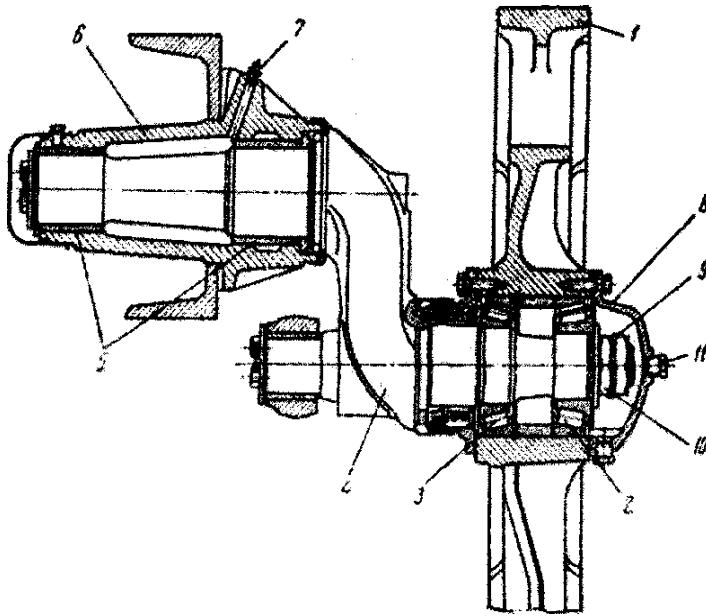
Напрявне колесо: 1 - напрявне колесо; 2, 3 - підшипники конічні; 4 - вісь колінчата; 5 - втулка; 6 - кронштейн напрямного колеса; 7 - оливниця; 8 - кришка; 9 - шайба стопорна; 10 - гайка регульовальна; 11 - пробка.
